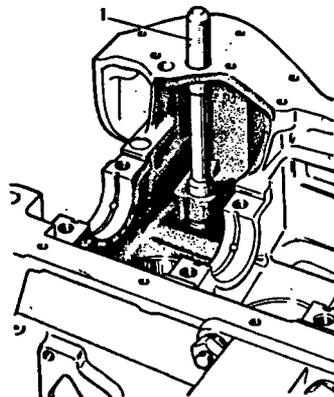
Выпрессовка втулки шестерни привода масляного насоса и распределителя зажигания: 1 - оправка А.60326/R
